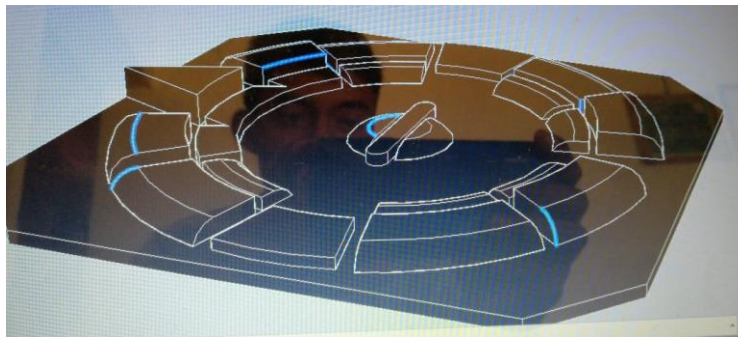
Diseño por computadora 3D de molde2 para ser fabricado con manufactura aditiva.
